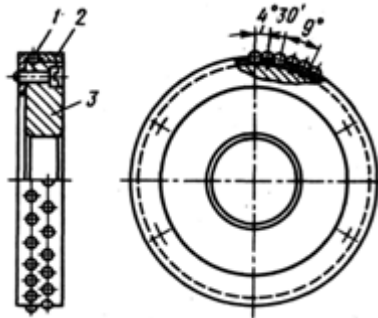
Инструмент центробежно-ударного действия для динамического упрочнения: 1 — рабочий шарик; 2 — корпус; 3 — сепаратор
